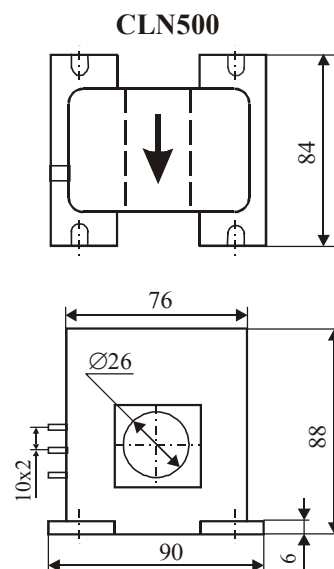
Внешний вид и габаритные размеры датчиков тока типа CLN-300SP1, CLN-500SP1
